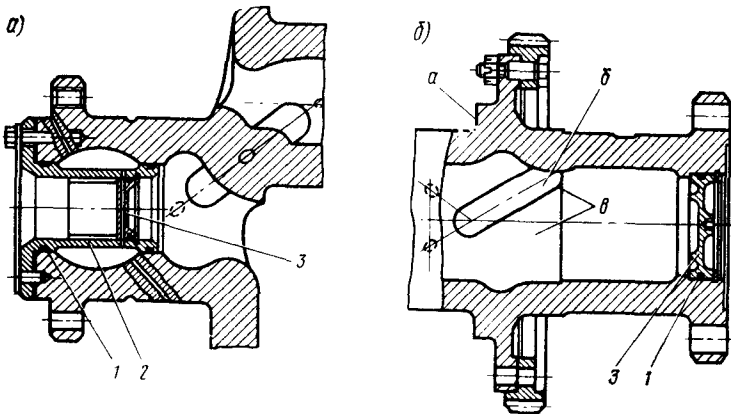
Концевые части коленчатого вала дизеля 1А-5Д49:
